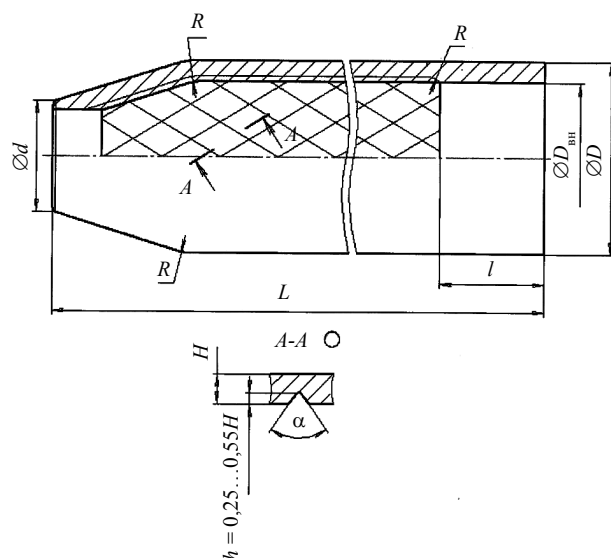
Внешний вид (сечение) корпуса. Заготовка корпуса для механической обработки до нарезания резьбы
